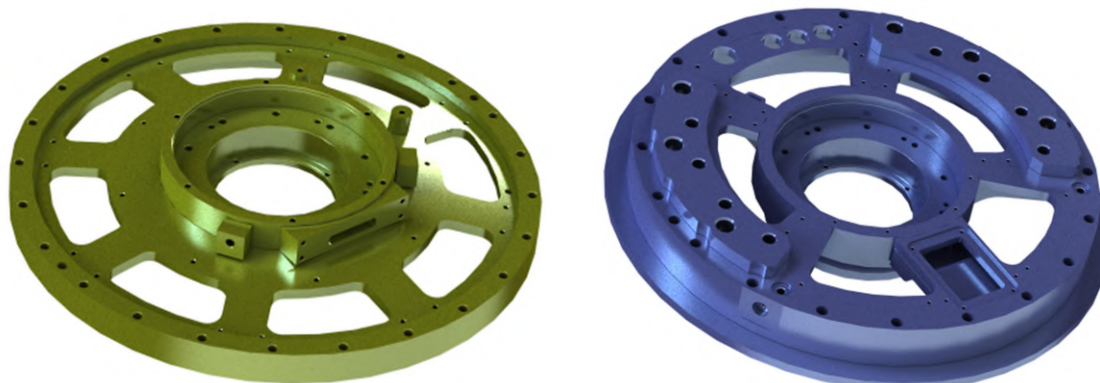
Модель ротора двигателя АТД-4450/6
